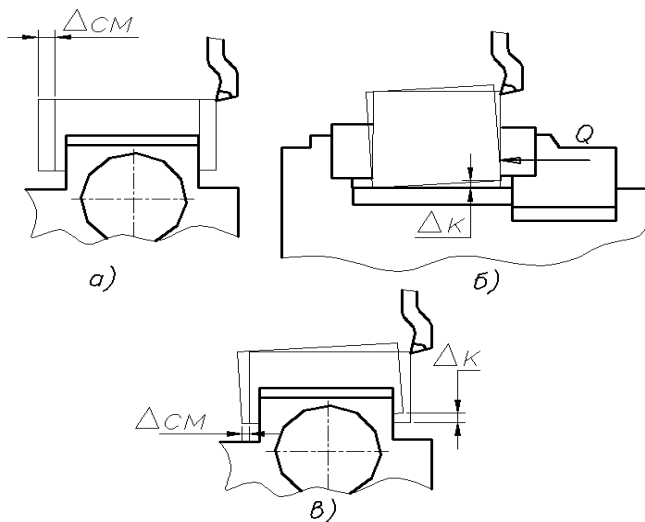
Схемы поведения заготовки при неправильном закреплении
